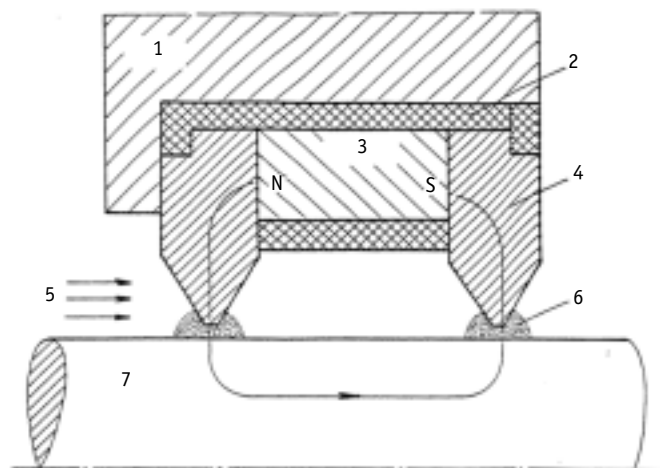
Принцип магнитного порошкового уплотнения: 1 - статор; 2 - немагнитная втулка; 3 - магнит; 4 - полюсные башмаки; 5 - избыточное давление; 6 - ферромагнитный порошок; 7 - ротор
